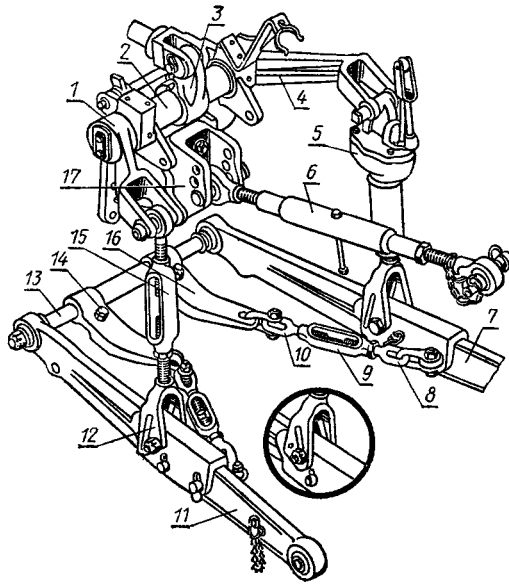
Навесное устройство тракторов МТЗ-80/82:
